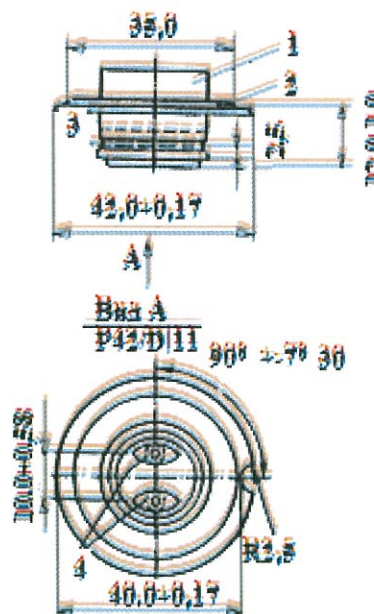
Цоколь P42D: 1 - внутренний стакан,
